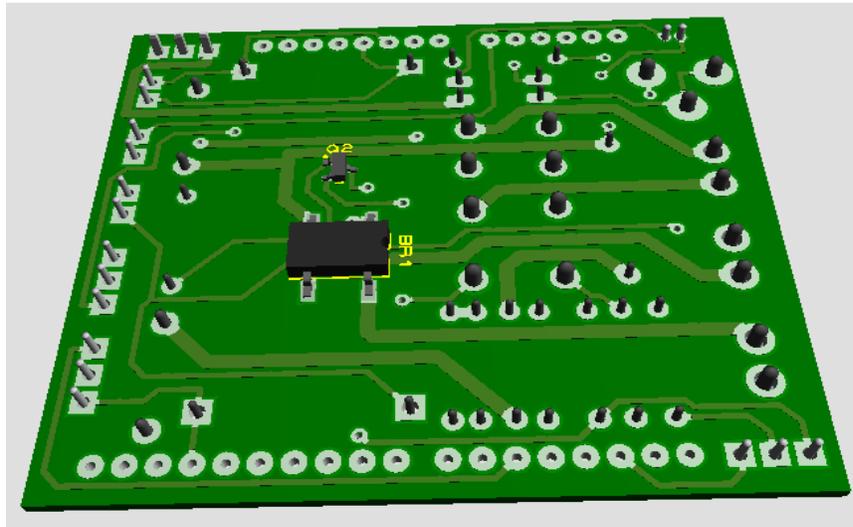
Tarjeta diseñada a dos capas para impresión en PCB vista posterior
